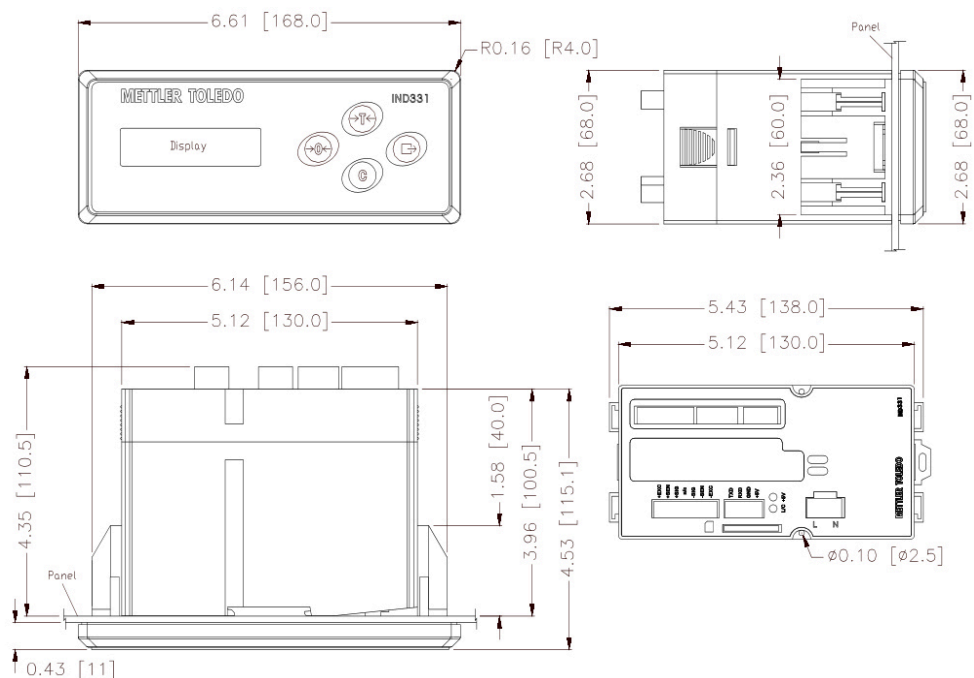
Dimensiones del gabinete de montaje en panel de la IND331
